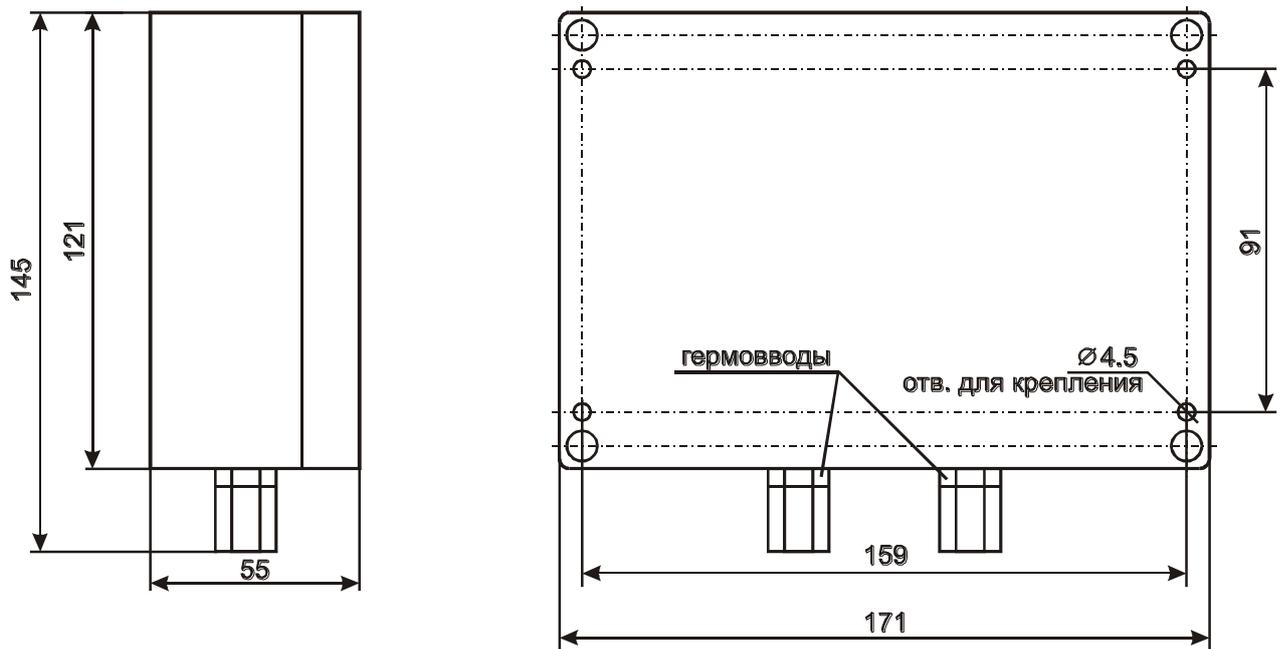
Внешний вид, габаритные и присоединительные размеры (исполнение IP65)
